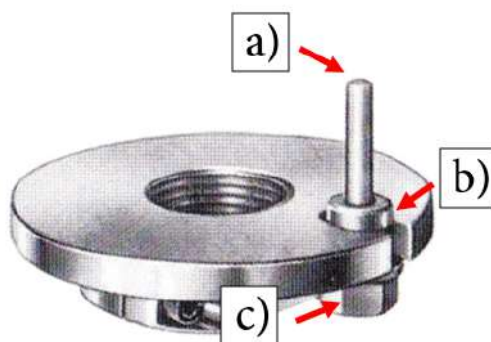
Prato de arrastamento: a) pino, b) fixador, c) porca; adaptado de [9].
